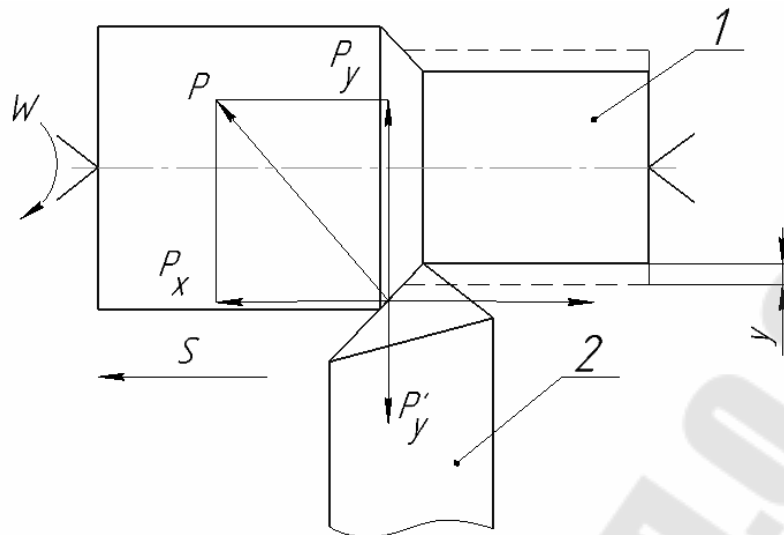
Схема обработки заготовки на токарном станке:
